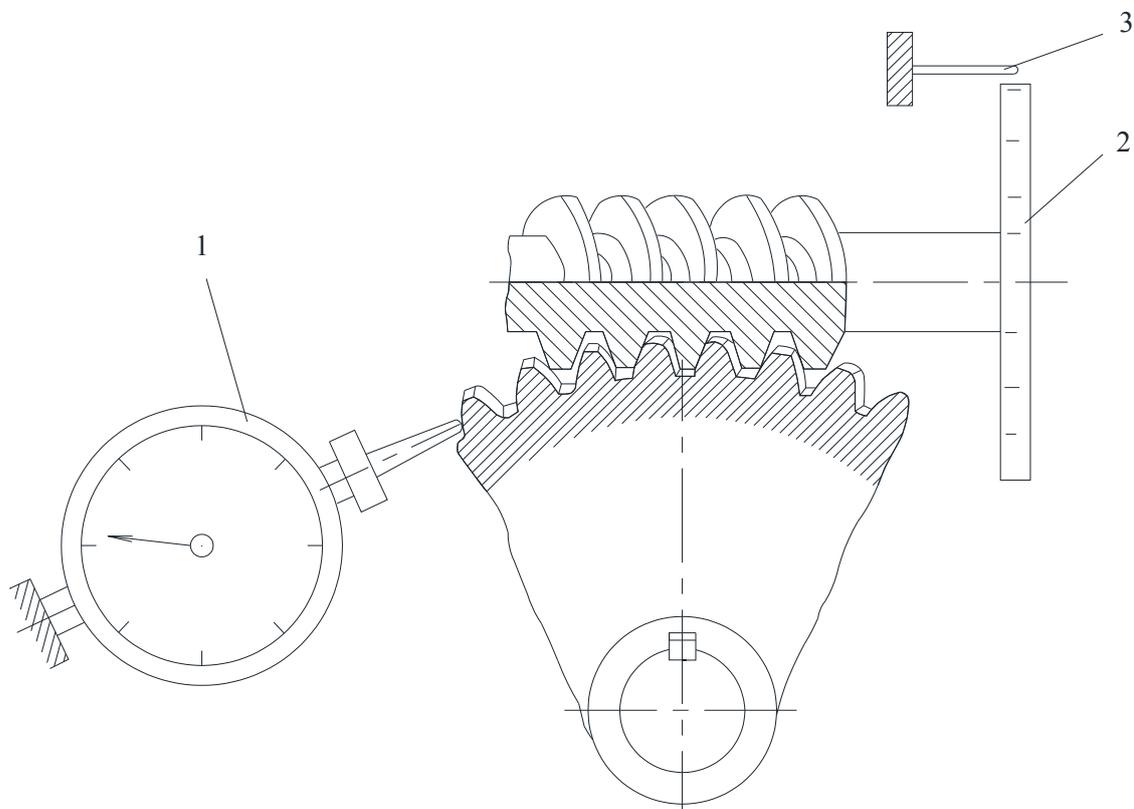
Проверка мёртвого хода червяка: 1 – индикатор; 2 – градуированный лимб; 3 – стрелка
